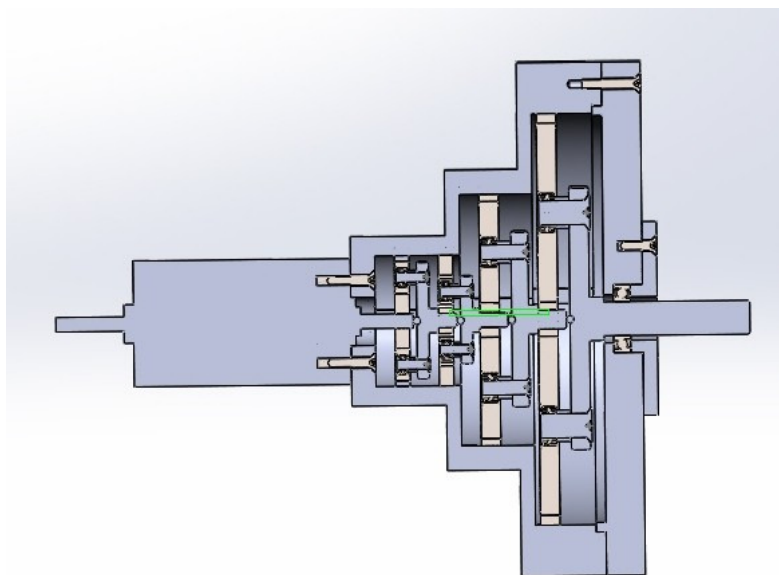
Четырехступенчатый редуктор привода управления запуском двигателя
